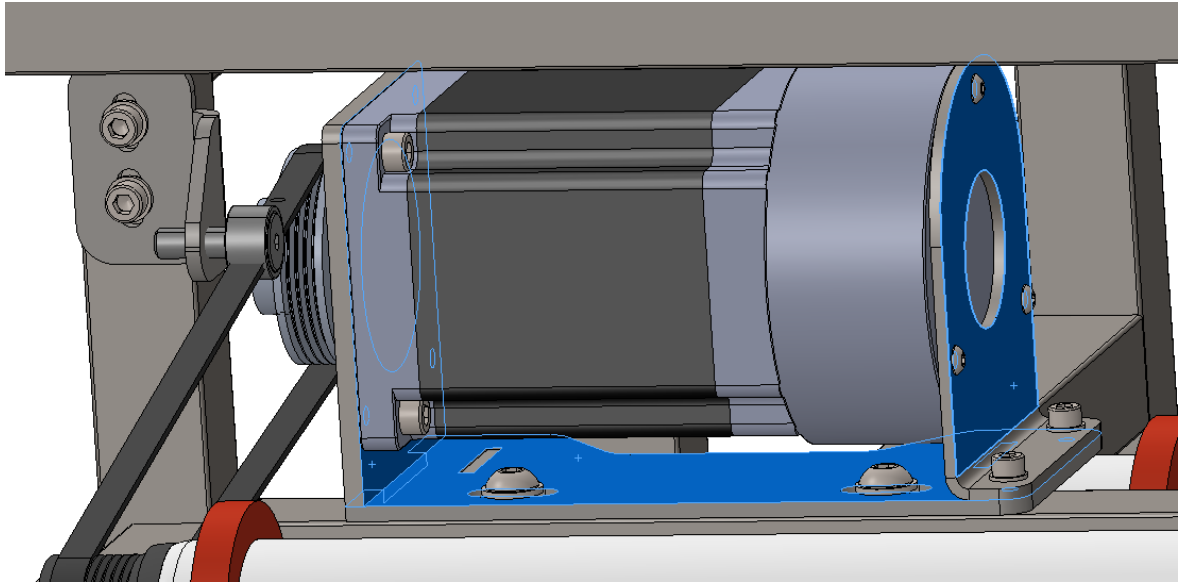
DETALLE DE ESTRUCTURA DE SUJECCIÓN DE NEMA 34
